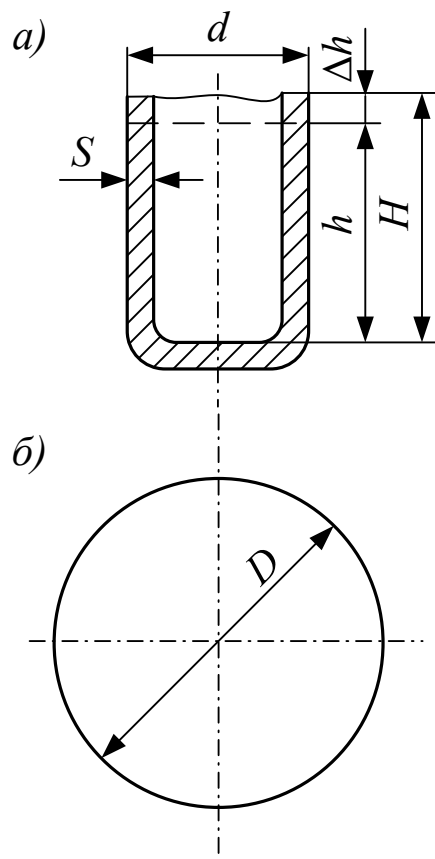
Деталь, виготовлена витягуванням, (а) та вихідна заготовка (б)
